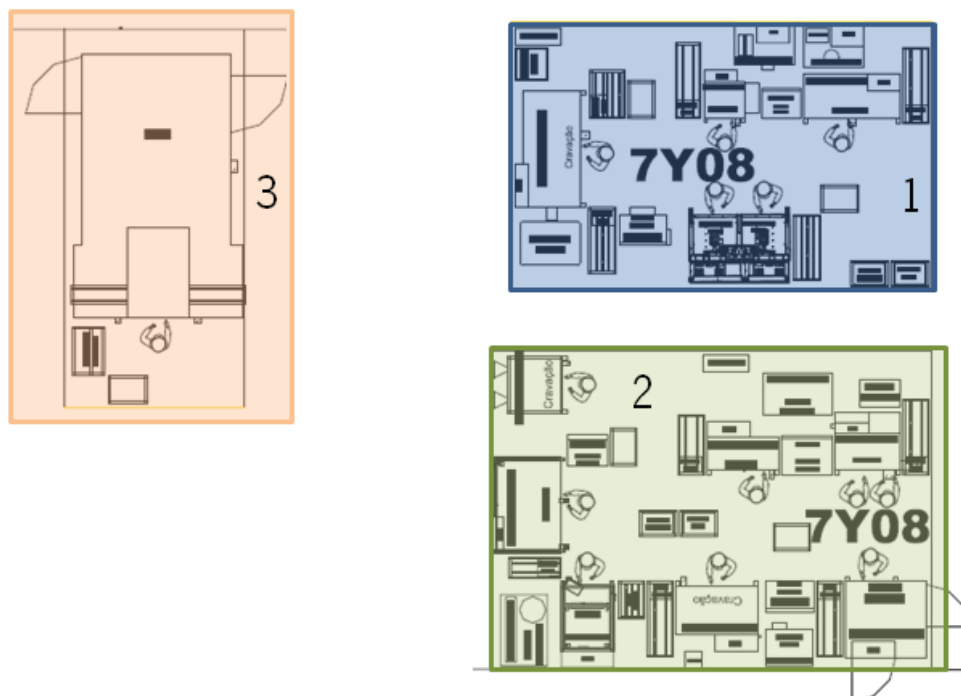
Layout da linha 7Y08: 1) Soldadura; 2) Cravação; 3) Máquina de soldadura CMT
